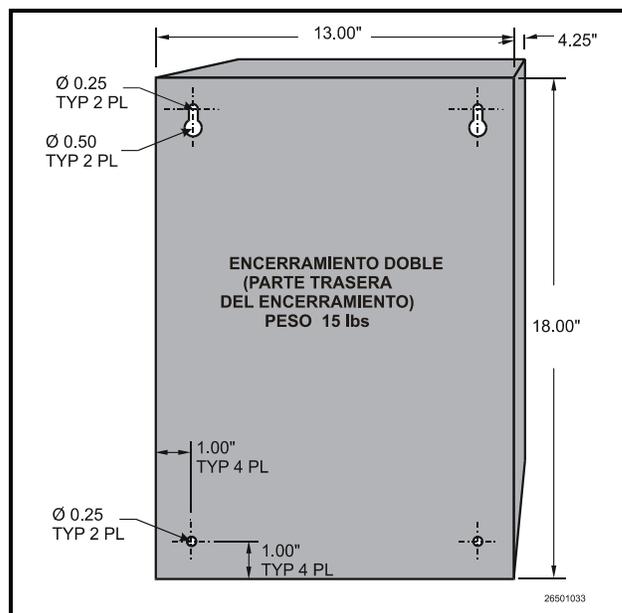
Dimensiones de Montaje de la Caja Doble
